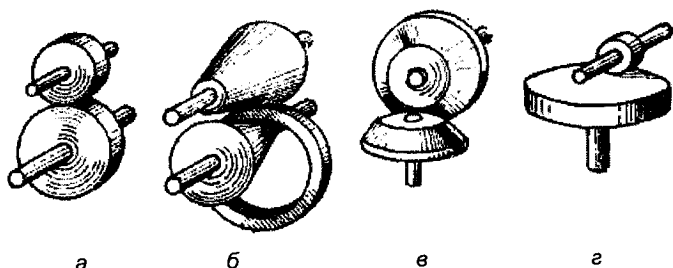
Види фрикційних передач: а – циліндрична; б та в – конічна; г – лобова
